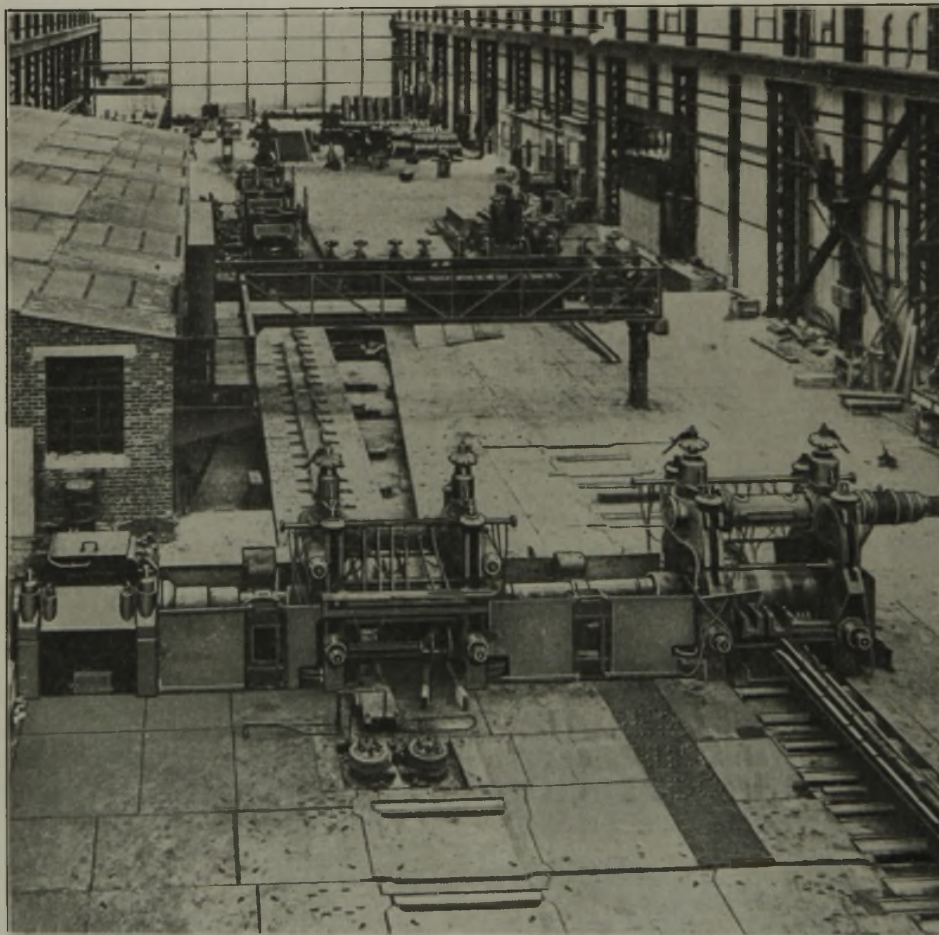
Vorstraße mit Stauchgerüst vor dem zweiten Gerüst.
